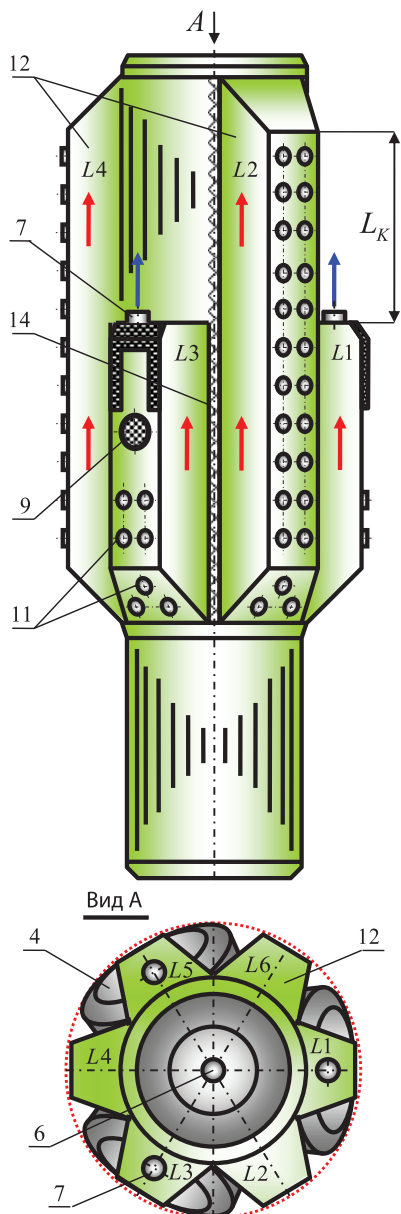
Общий вид корпуса наддолотного калибратора-эжектора
